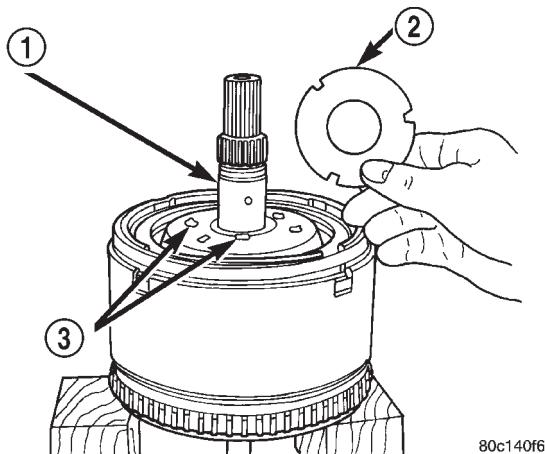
Desmontaje del conjunto de embragues de impulsión
